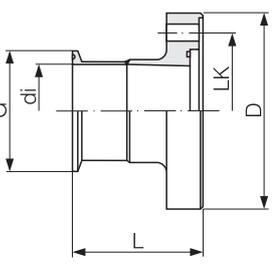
Abmessungen Frontansicht Messaufnehmer DN 40...100
